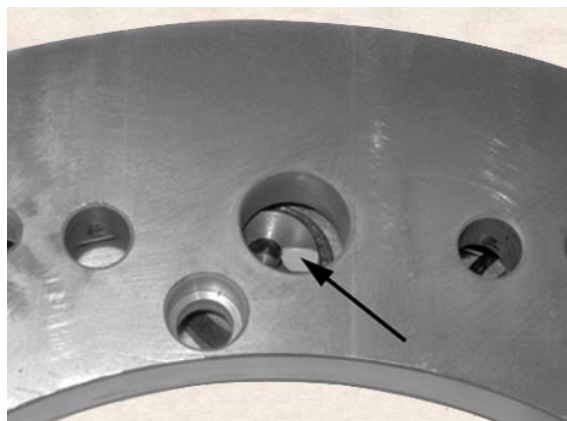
Когда планшайба вращается, проверьте, вращаются ли подшипники наблюдая за метками на подшипниках.
